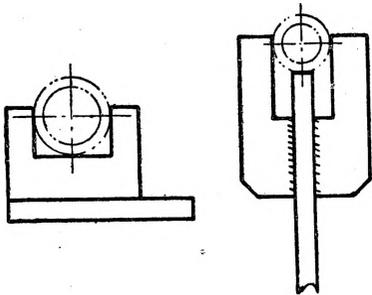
Конструкции призм для упрощенной установки цилиндрических деталей.
